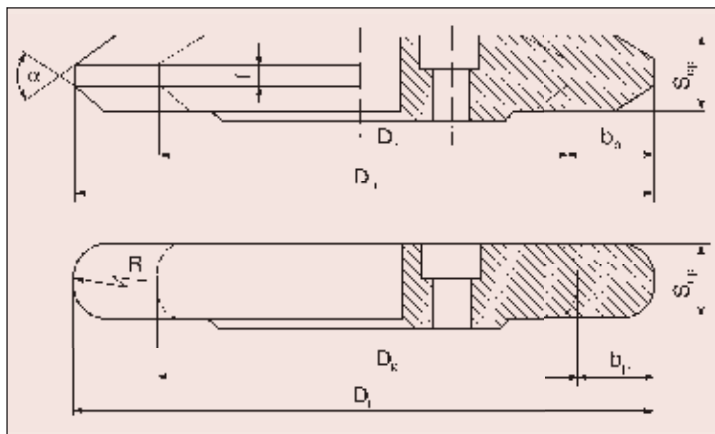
Ролики с цилиндрической (а) и сферической (б) рабочей поверхностью
